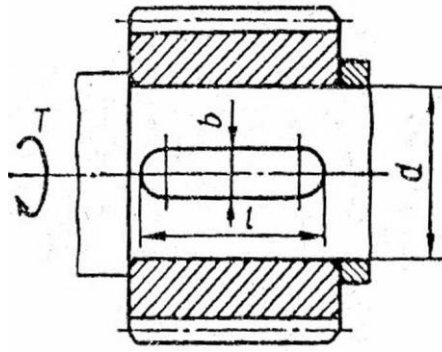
З'єднання вала із зубчастим колесом за допомогою призматичної шпонки.
